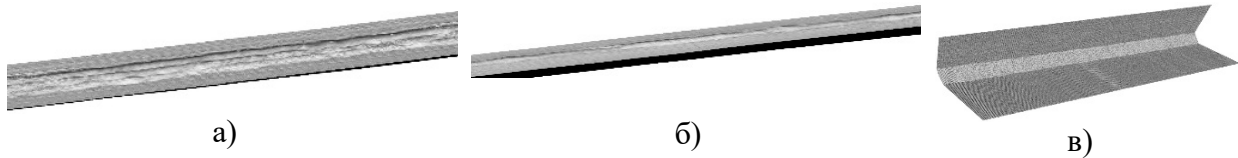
Визуализация цифровой реплики лицевой (а), корневой (б) поверхности стыкового сварного шва и лицевой (в) поверхности углового сварного шва КСС.
